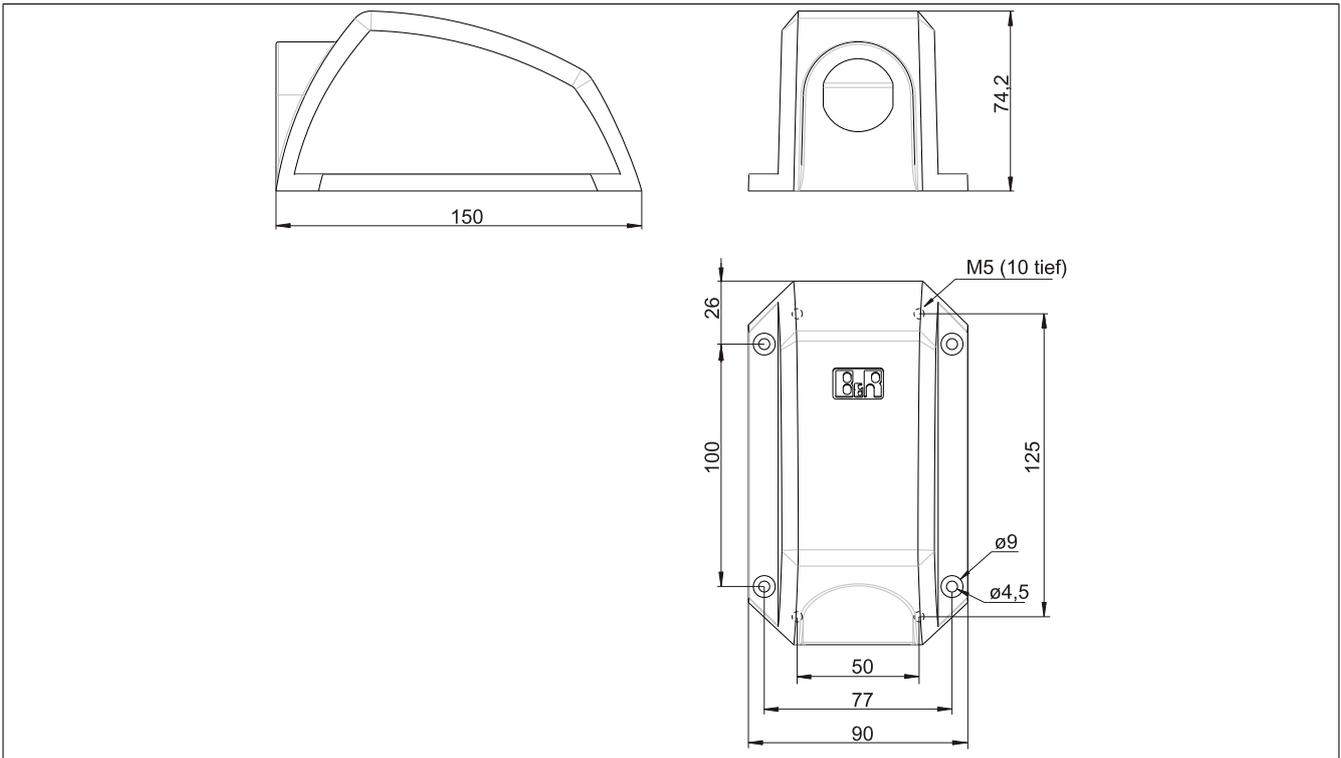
4MPCBX.0001-00 - Abmessungen
